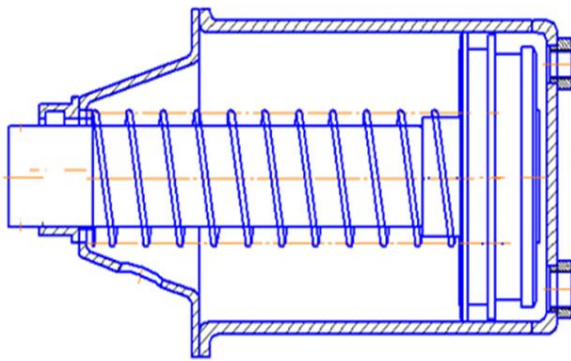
Тормозной цилиндр тепловоза ЧМЭЗ
